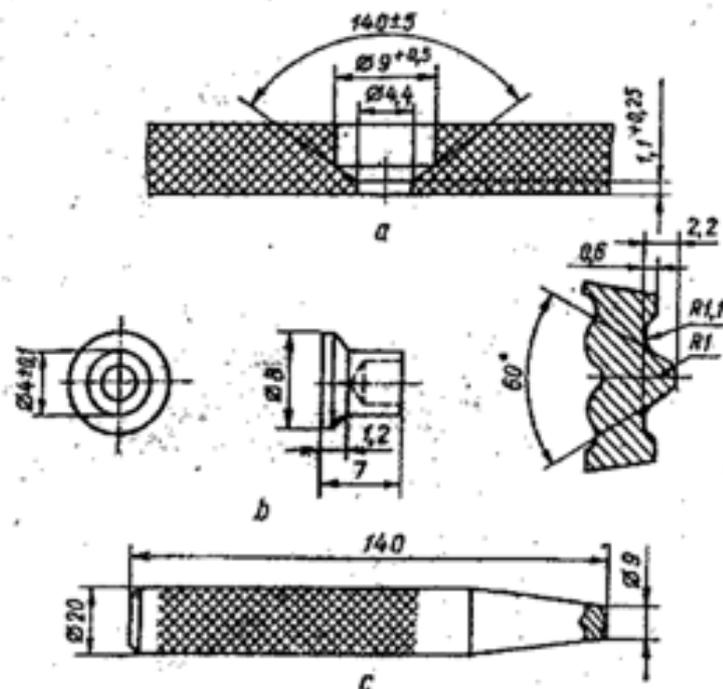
Инструмент для заклепки фрикционных накладок на тормозные колодки задних колес: а - отверстие в накладке; б - размеры заклепки; в - оправка для расклепывания заклепок.
